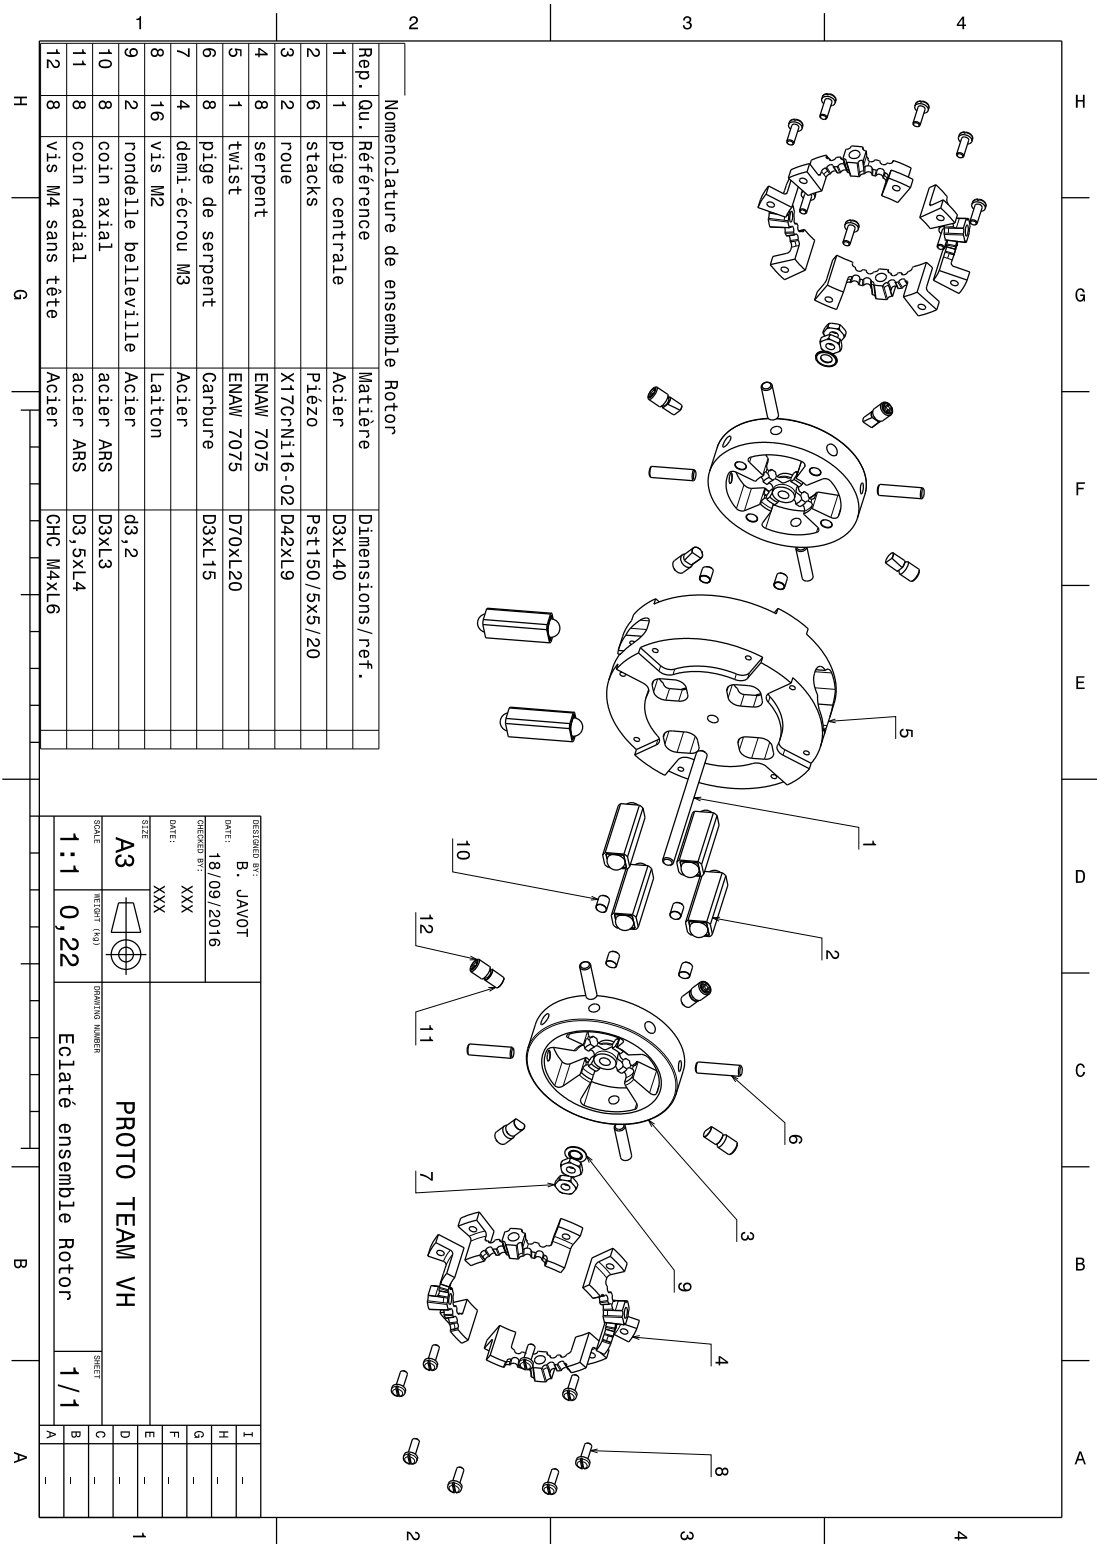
Ensemble Rotor : twist, serpents, roues, pige centrale, stacks.
